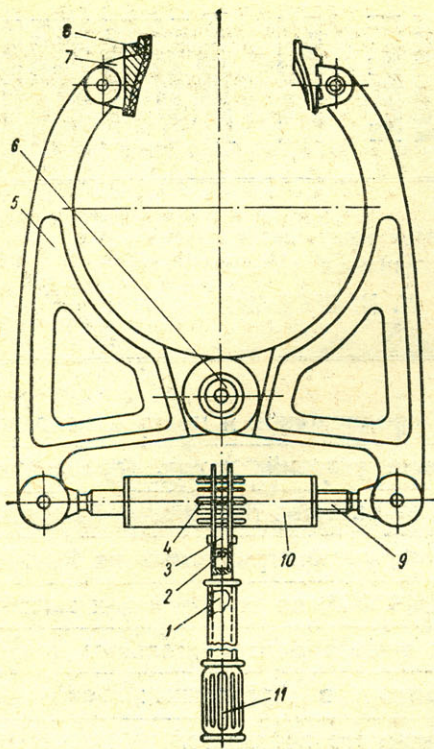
Монтажный домкрат для шин: 1 — рукоятка; 2 — пружина собачки; 3 — собачка; 4 — храповик; 5 — захваты; 6 — шарнир; 7 — опоры; 8 — вкладыши; 9 — винтовой тандер; 10 — муфта; 11 — удлинитель.
